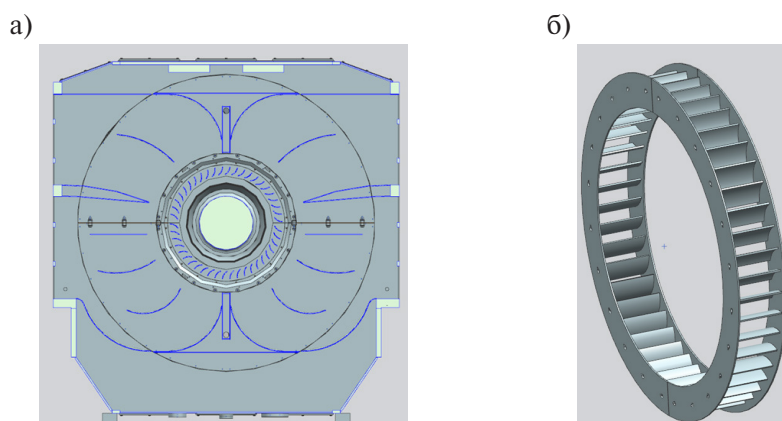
Подводящий канал ротора (а) и неподвижный направляющий аппарат ротора (б)
